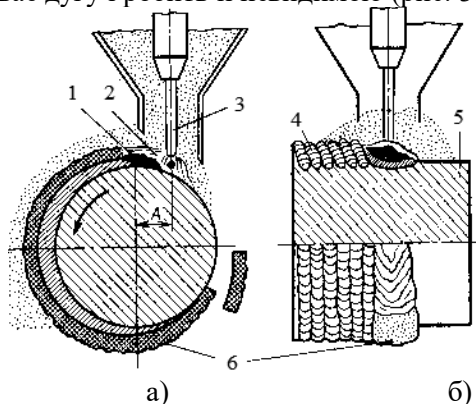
Схема наплавлення під шаром флюсу: а – поперечний переріз; б – поздовжній переріз; 1 – ванна розплавленого металу; 2 – розплавлений флюс; 3 – електродний дріт; 4 – наплавлений шар металу; 5 – деталь; 6 – шлакова кірка; А – зміщення електродного дроту із зеніту
